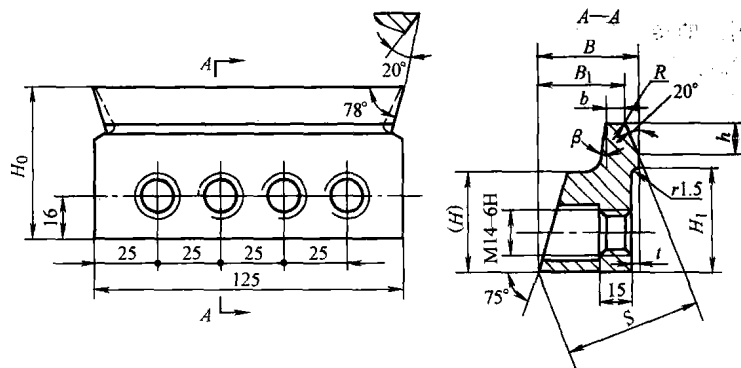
IV型锥齿轮精刨刀尺寸 (m=3~20mm)
